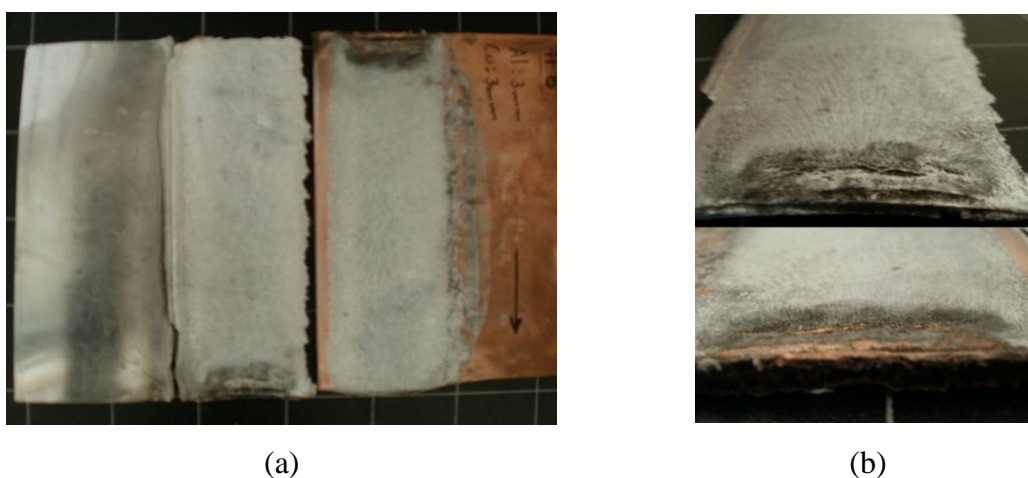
(a) Soldadura UEW4; (b) Detalhes da zona inicial da soldadura e do padrão observado.
